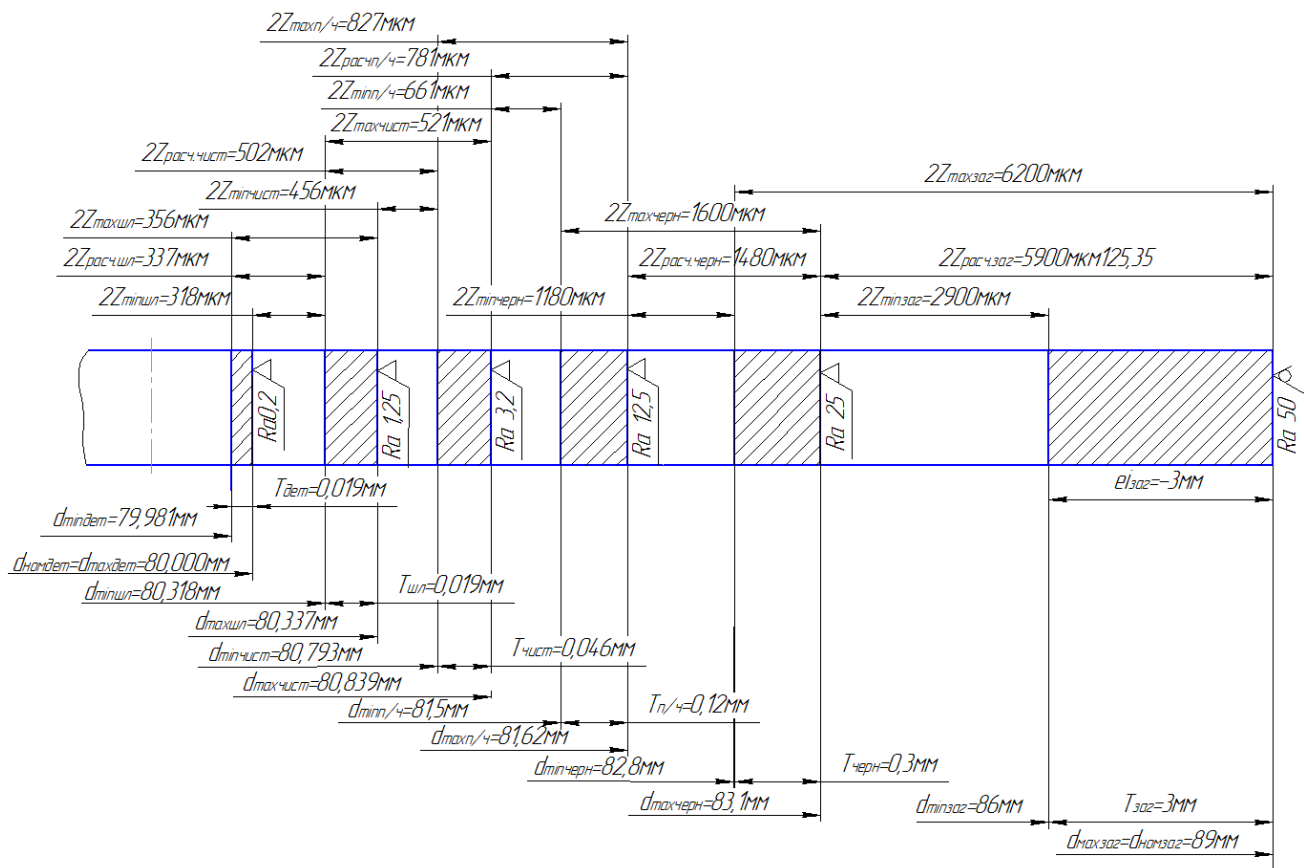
Схема расположения припусков и допусков для поверхности 80h6
